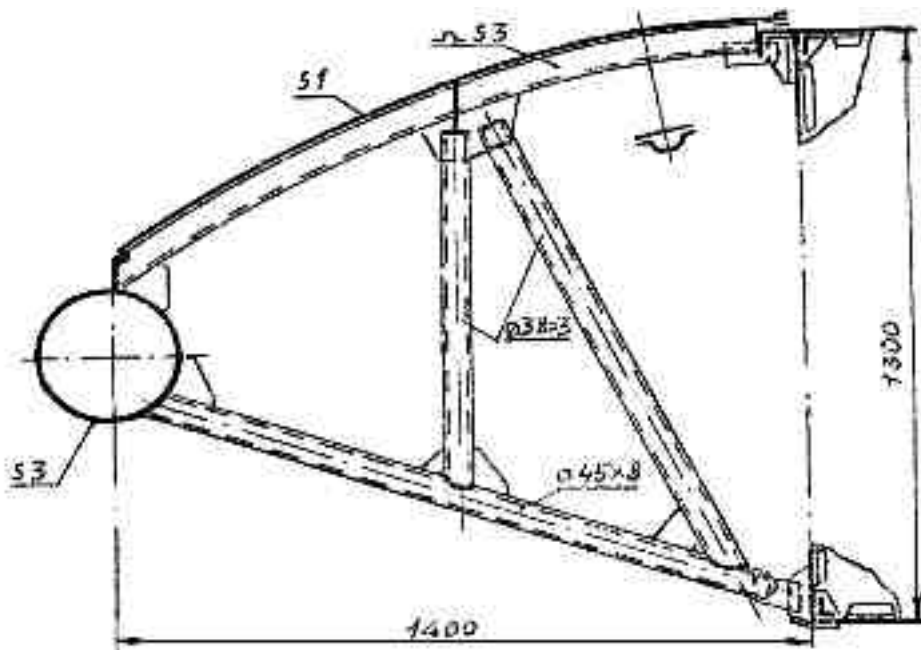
Поперечный разрез периферийного бортового ресивера СВП
